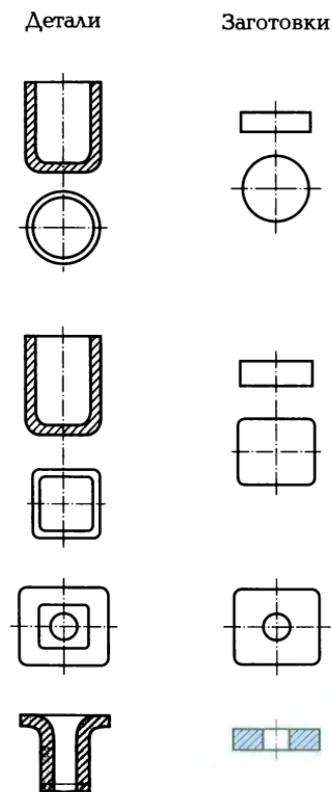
Детали различных конфигураций и заготовки для получения этих деталей при холодном выдавливании
